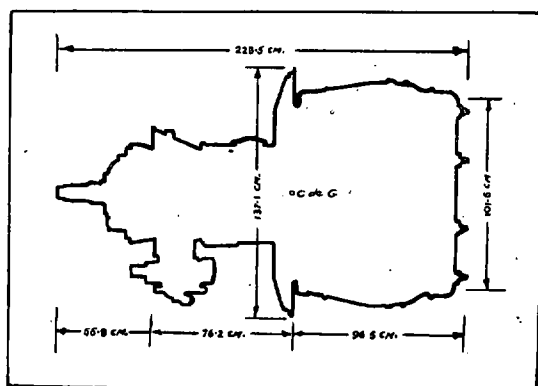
Dimensiones del motor (sin la tobera de salida).
